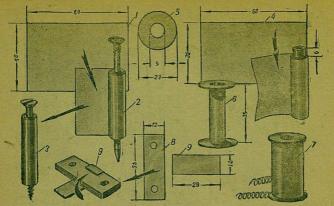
Детали пишущего реле: 1— полоска жести, которой обертывается гвоздь или шуруп, 2— обертывание гвоздя, 3— готовая спаянная обертка, 4— полоска бумажной ленты для гильзы катушки, 5— щеки катушки, 6— готовая гильза катушки, 7— готовая катушка, 8— жестяная пластинка ярма, 9— обойма ярма (продолжение рис. 46 и подписи см. на следующей странице).
